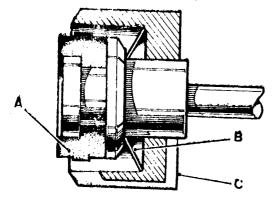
13 - Montaje de la empaquetadura de la válvu la.
